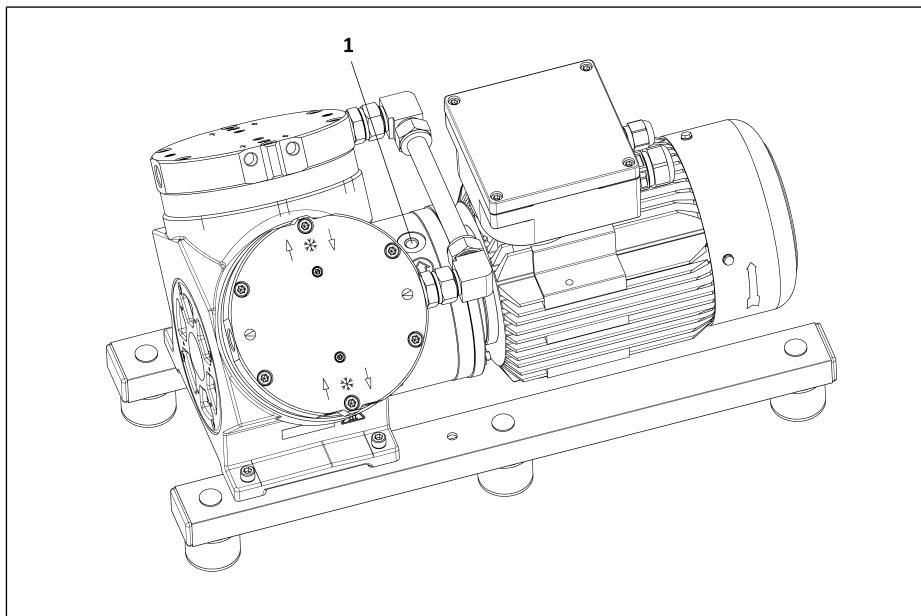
M12-Schraube herausschrauben (dargestellte Pumpe beispielhaft)
